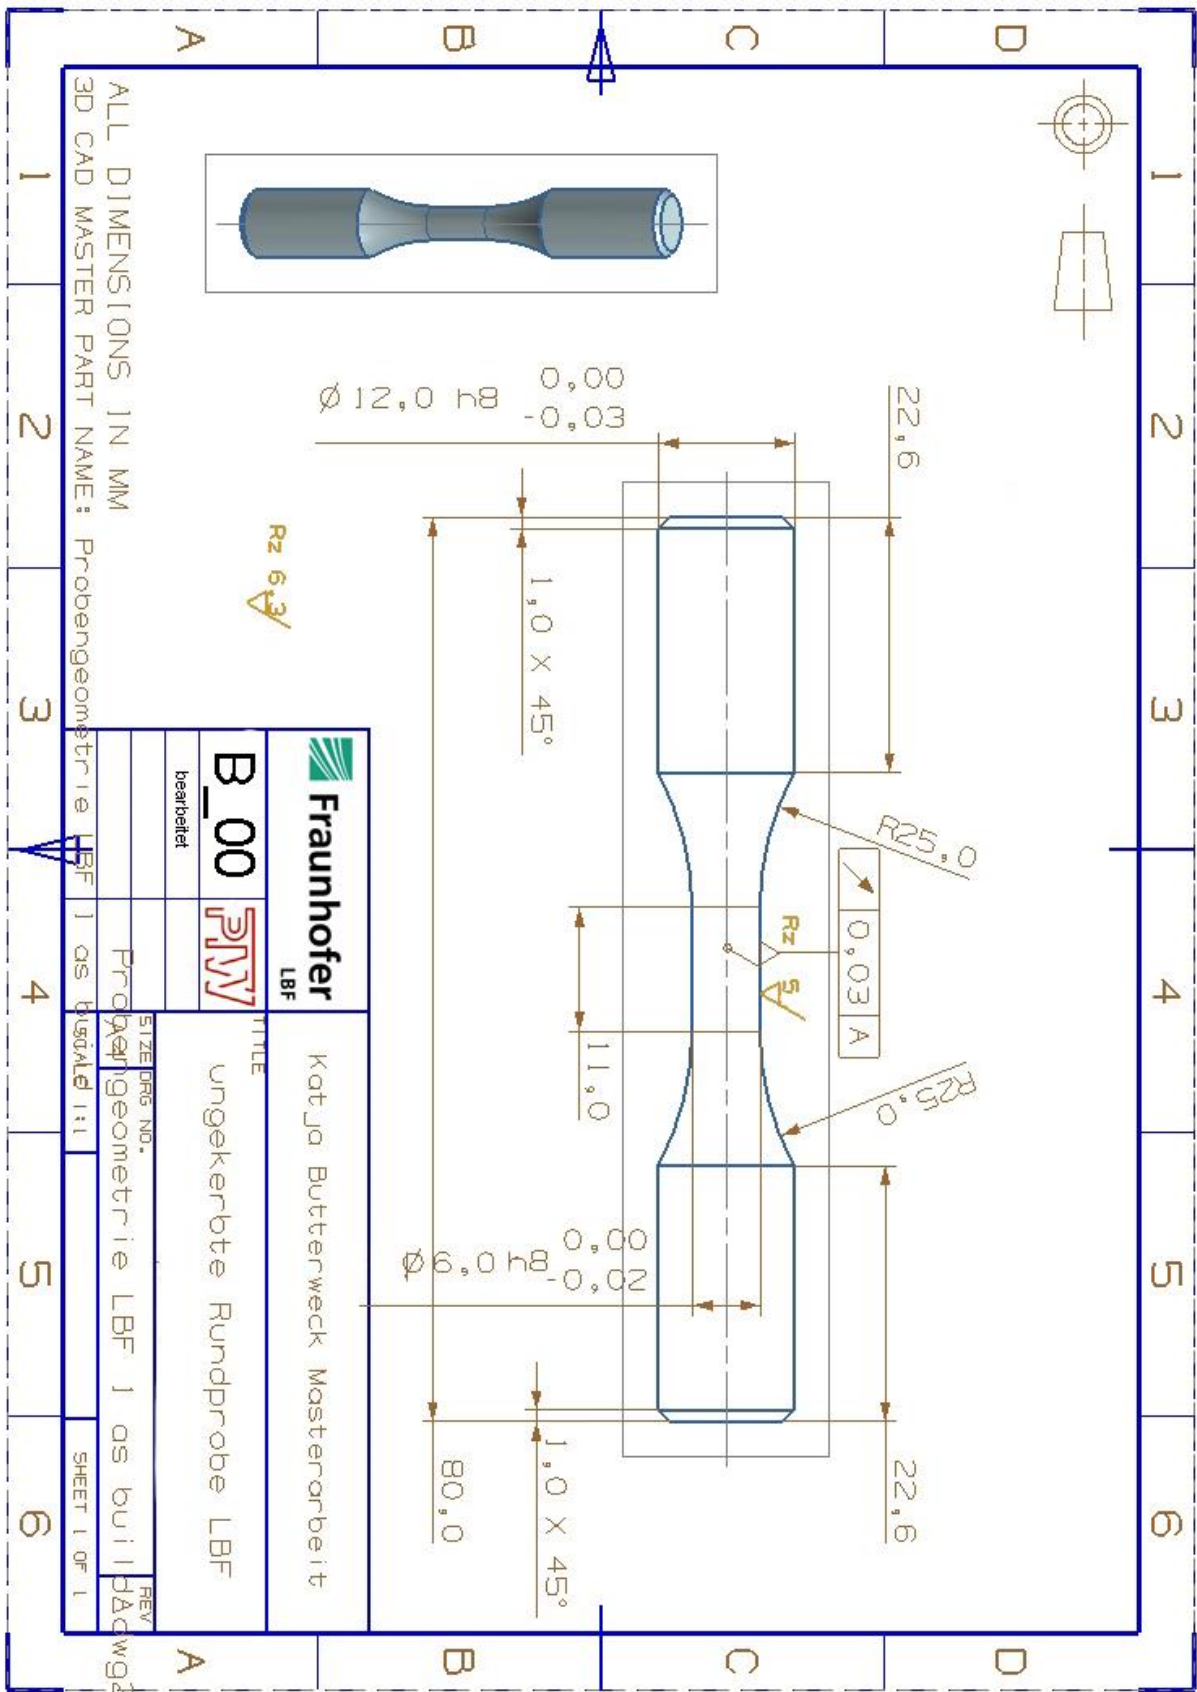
Technische Zeichnung Probengeometrie D_00 bearbeitet
